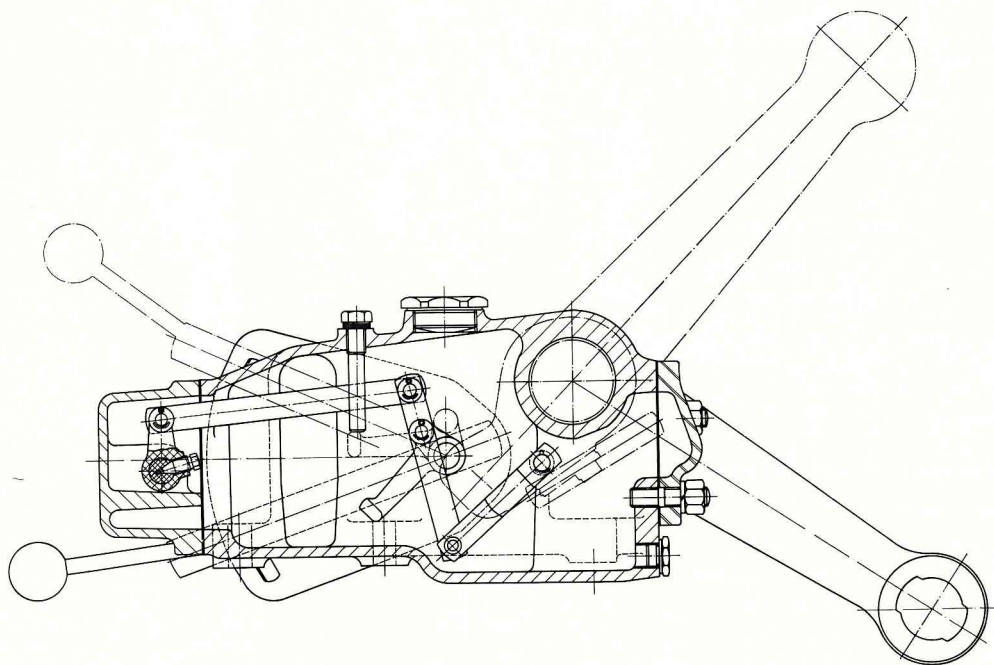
Smontaggio del corpo distributore dal sollevatore idraulico.
